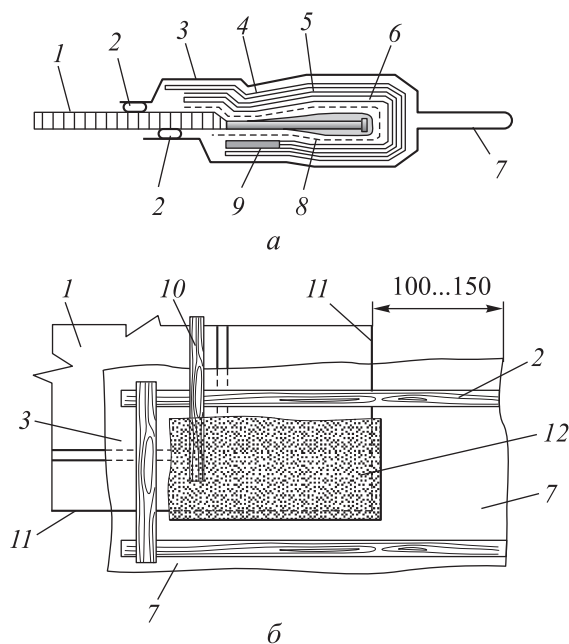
Схемы сборки ВМ при ремонте повреждений на кромке детали:
